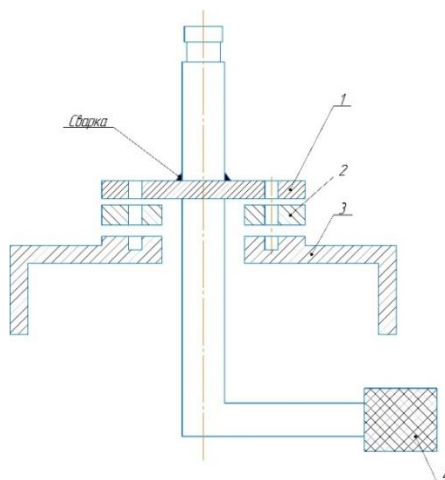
Модернизируемая часть насоса: 1- трубка с фланцем; 2 – резиновая прокладка; 3 – корпус бака; 4 – заборный сетчатый фильтр
